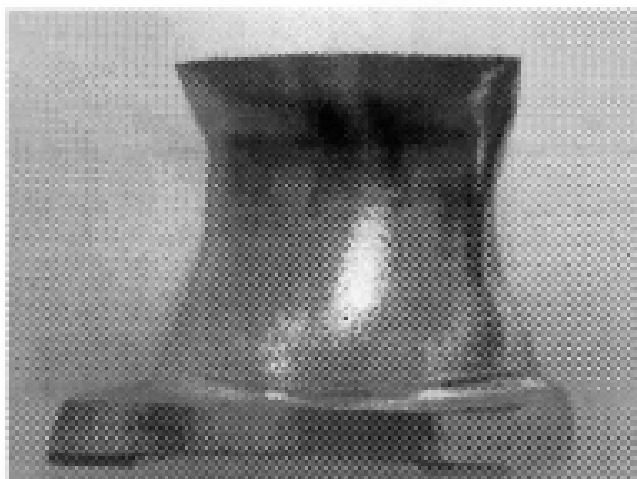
Зовнішній вигляд компресорної лопатки виготовленої
